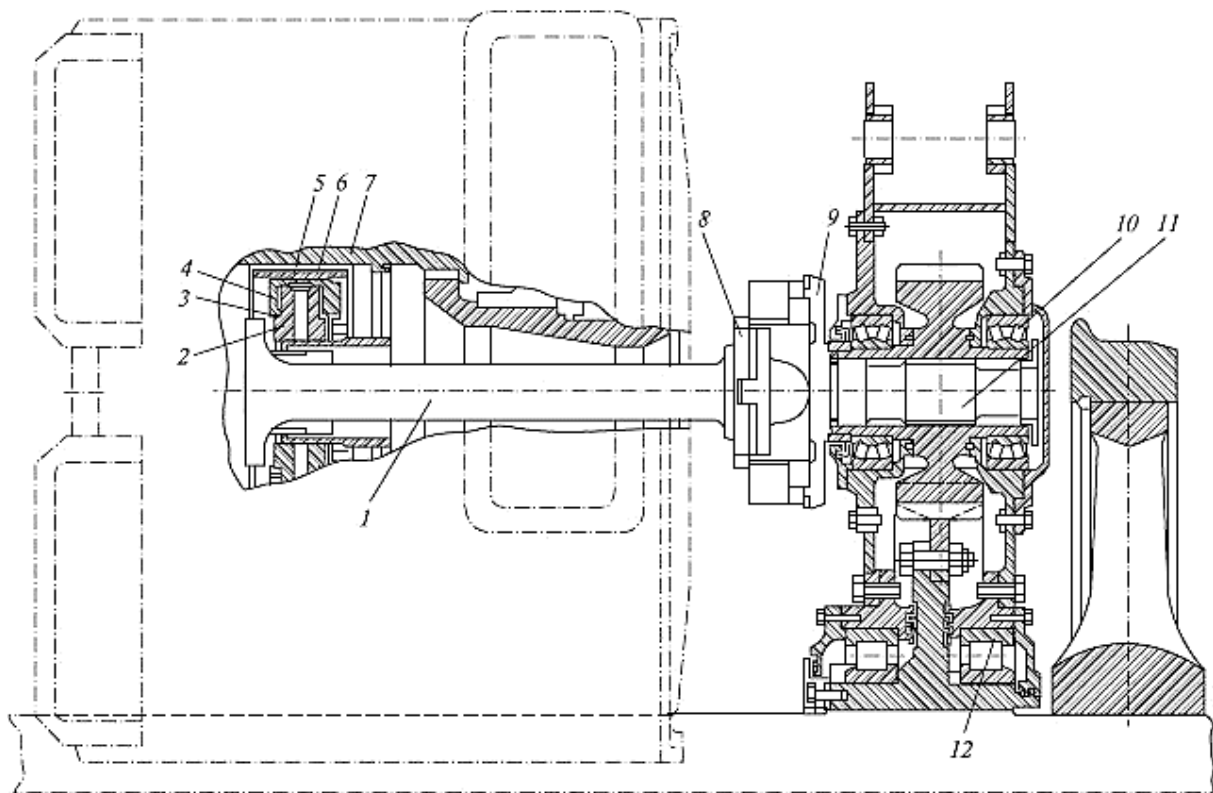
Редуктор і карданний привод електровоза ЧС4Т:
